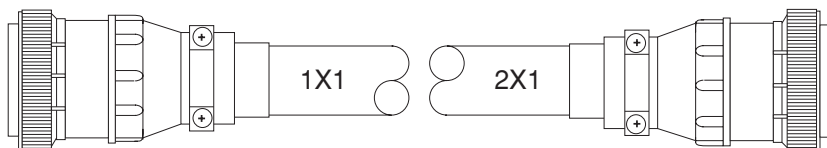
Collegamenti dall'alimentatore alla consolle RHF ed al tavolo di lavoro
